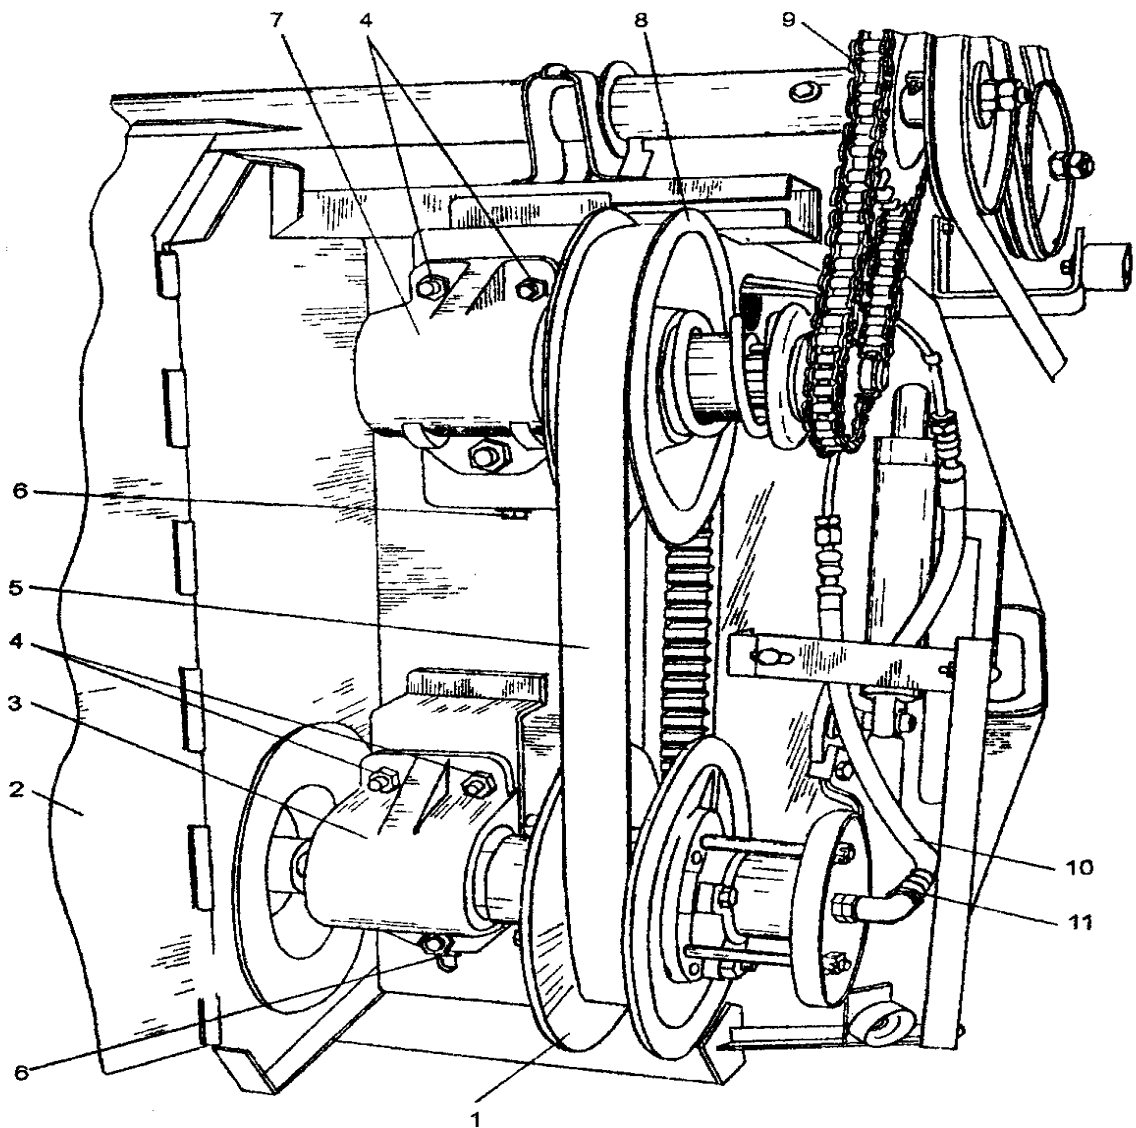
Вариатор мотовила: 1 – шкив вариатора нижний; 2 – щиток защитный; 3, 7 – корпуса; 4, 11 – гайки; 5 – ремень; 6 – болты натяжные; 8 – шкив вариатора верхний; 9 – цепь; 10 – рукав
